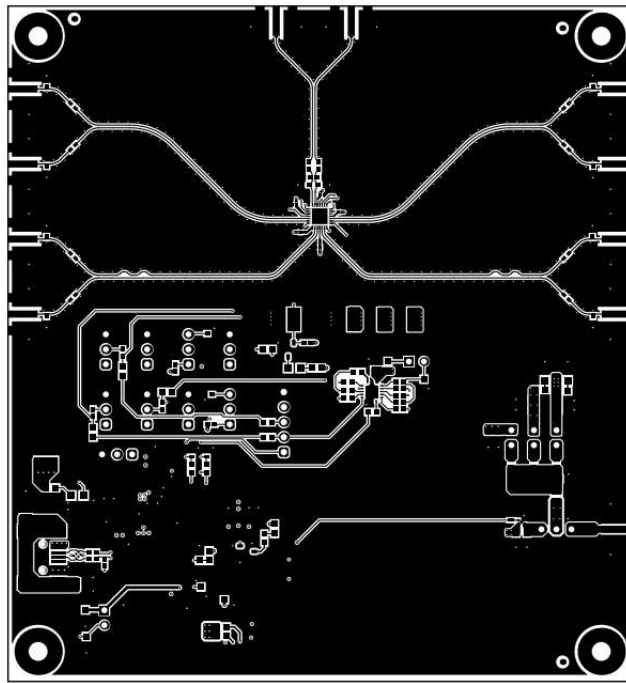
顶层 ( CLKIN / CLKOUT 信号 )
